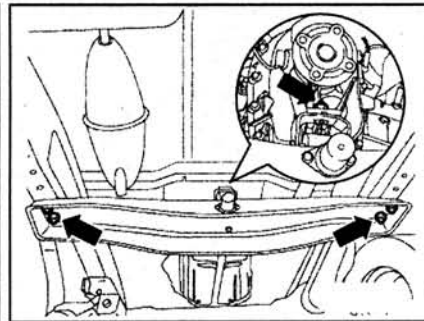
Установите подъемник V.A.G 1383 A под коробку передач и поднимите ее. Открутите болты крепления (стрелки) поперечной балки двигателя/коробки передач и снимите ее.
